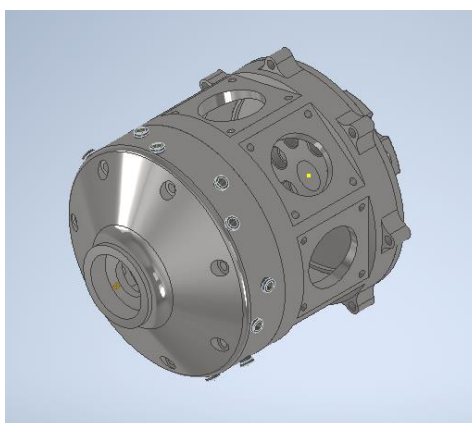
Diseño completo del bloque motor mediante Autodesk Inventor
